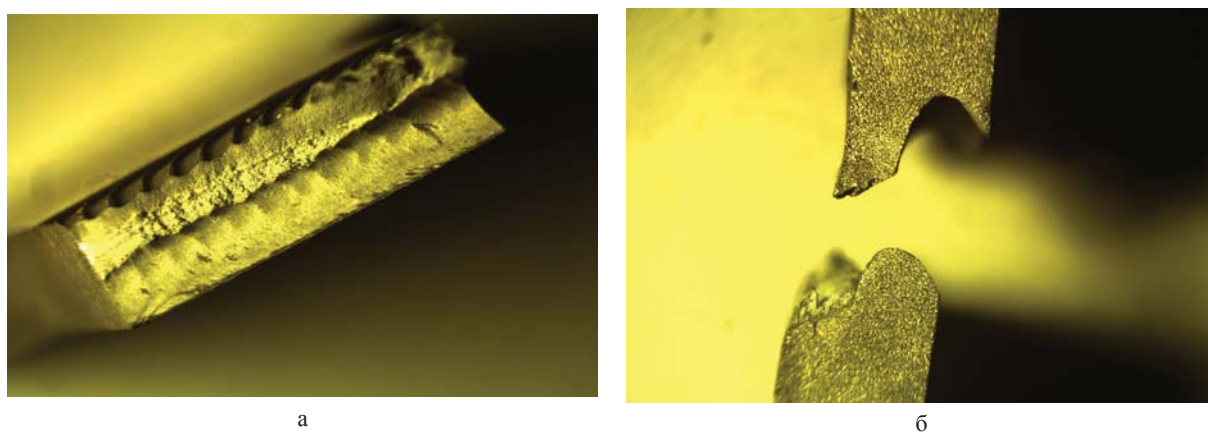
Разрушенный образец со сварным соединением (режим 2): а — вид сверху; б — вид сбоку
